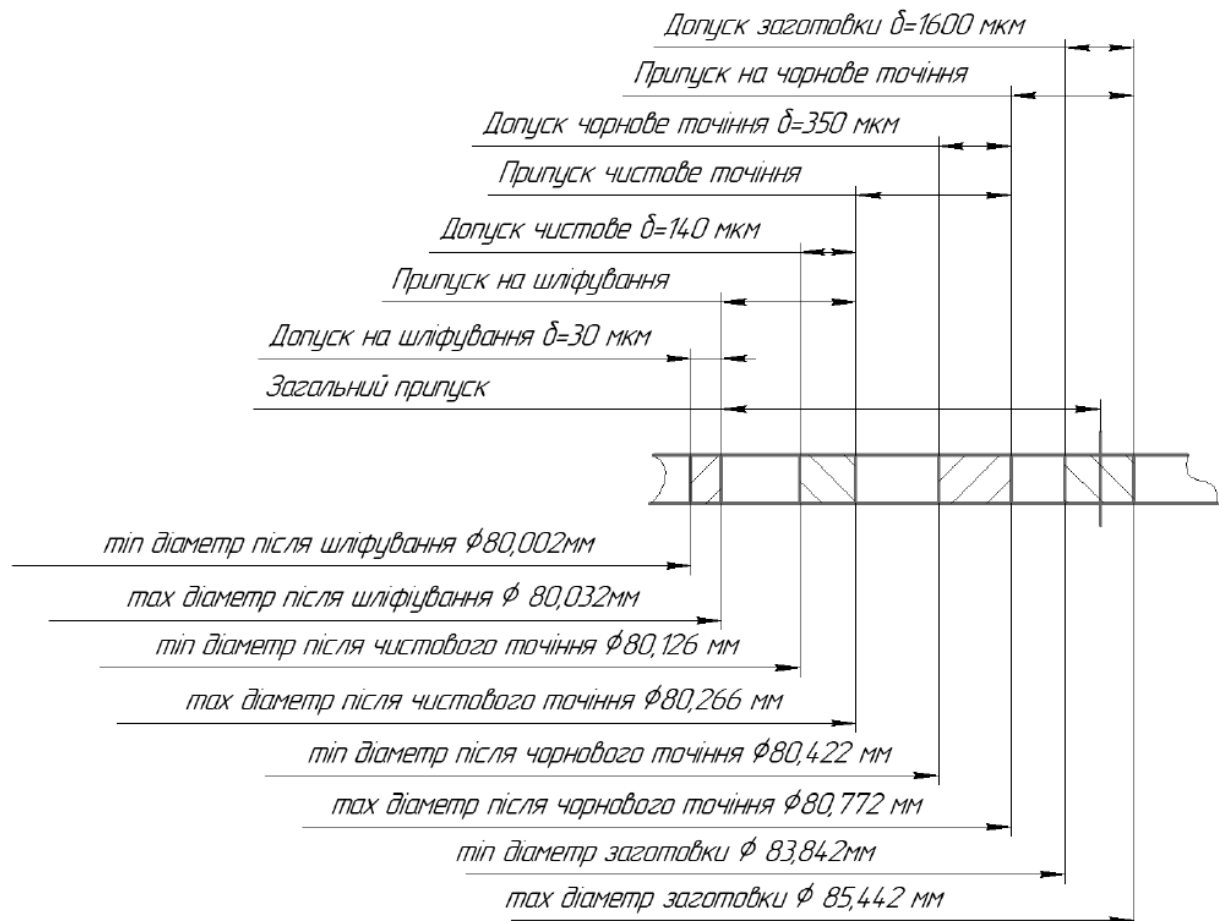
Схема розміщення полів допусків для розміру $\varnothing 80k7^{(+0,032 / +0,002)}$
